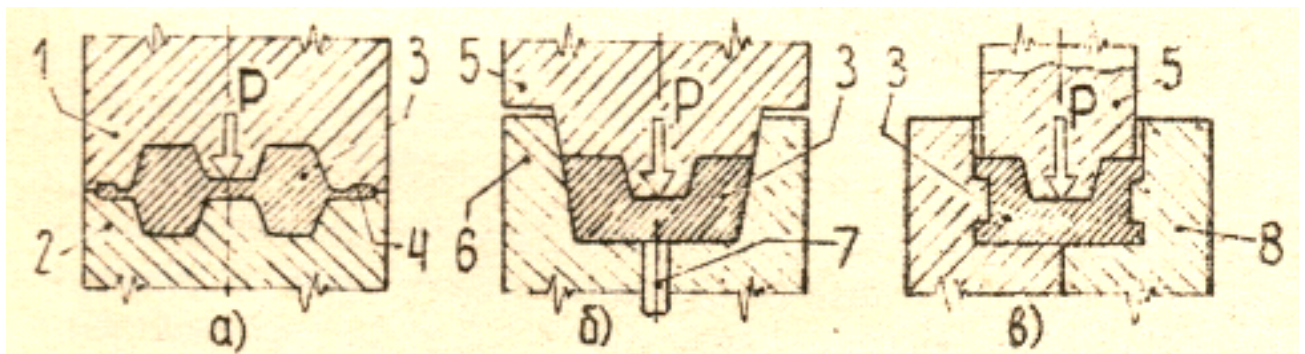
Схема горячей объемной штамповки: 1 и 2 — верхний и нижний штампы; 3 — поковка; 4 — облой; 5 — пуансон; 6 — матрица; 7 — выталкиватель; 8 — матрица разъемная
